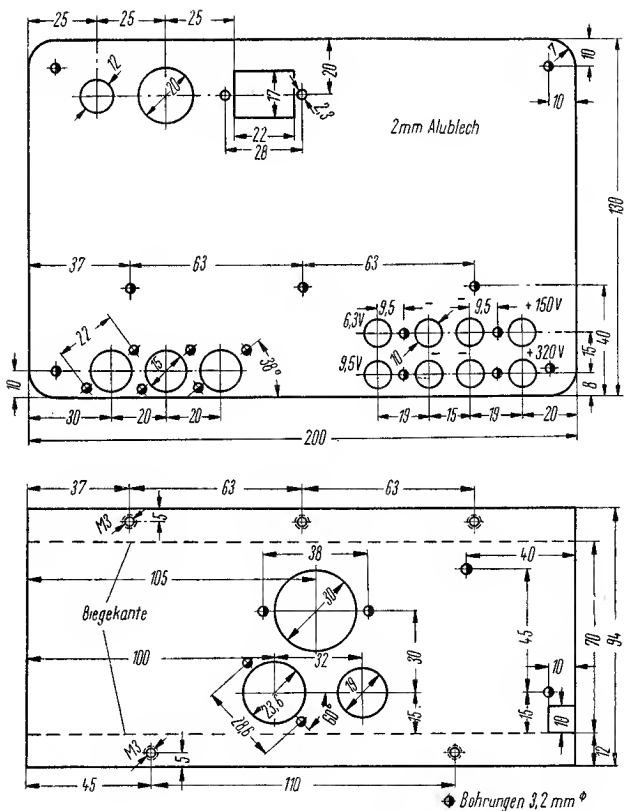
Maßskizze und Bohrplan für Frontplatte (oben) und Chassis (unten) des Universal-Netzgerätes
